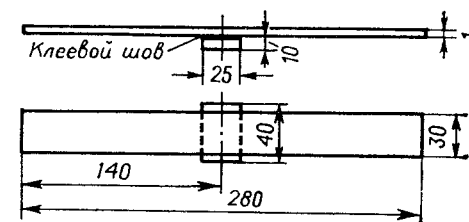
Стандартный образец для испытаний прочности при неравномерном отрыве.
